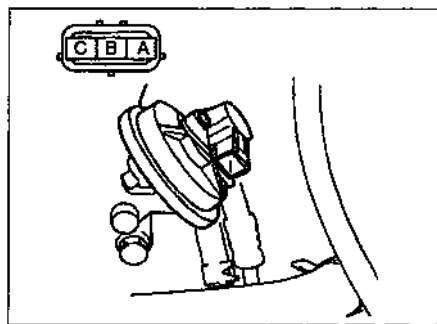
Детали разъема датчика положения клапана рециркуляции
